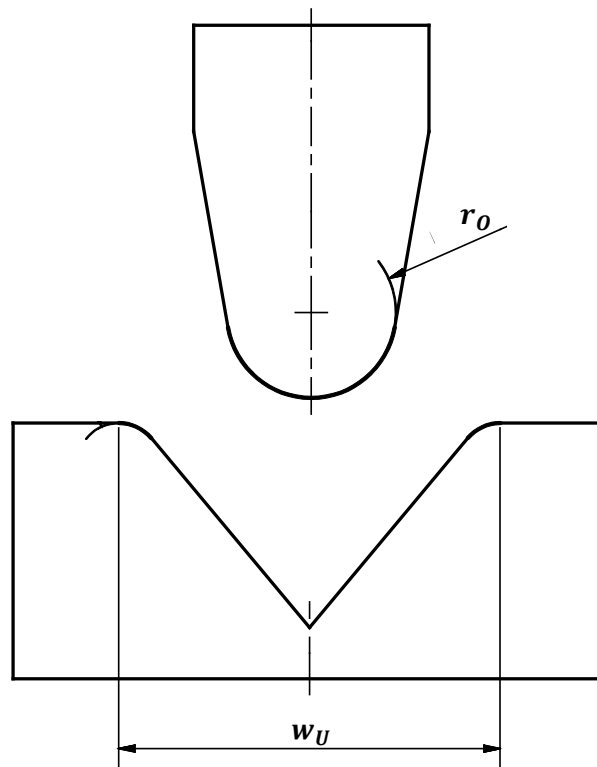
Definition der Geometrieparameter am Ober- und Unterwerkzeug beim Gesenkbiegen
